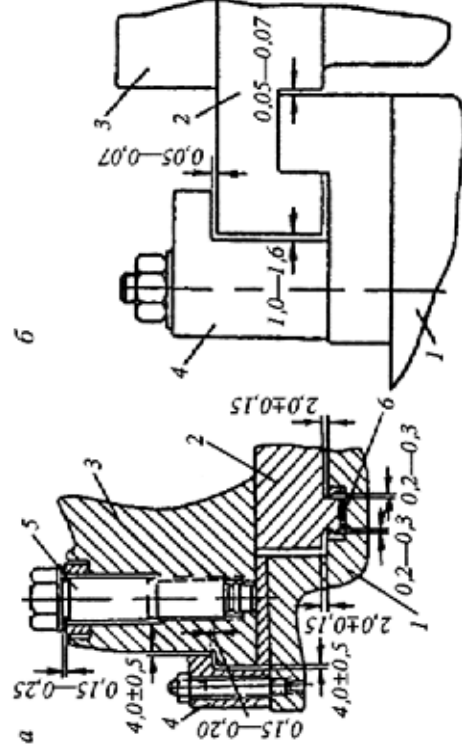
Соединение консольных лап литых цилиндров с корпусами выносных подшипников: *a* – у турбины К-300-240 ХТЗ; *б* – у турбин конструкции ЛМЗ, ТМЗ; 1 – корпус подшипника; 2 – лапа нижней половины цилиндра, 3 – лапа крышки цилиндра, 4 – «г-образные» шпонки, 5 – отжимной болт
